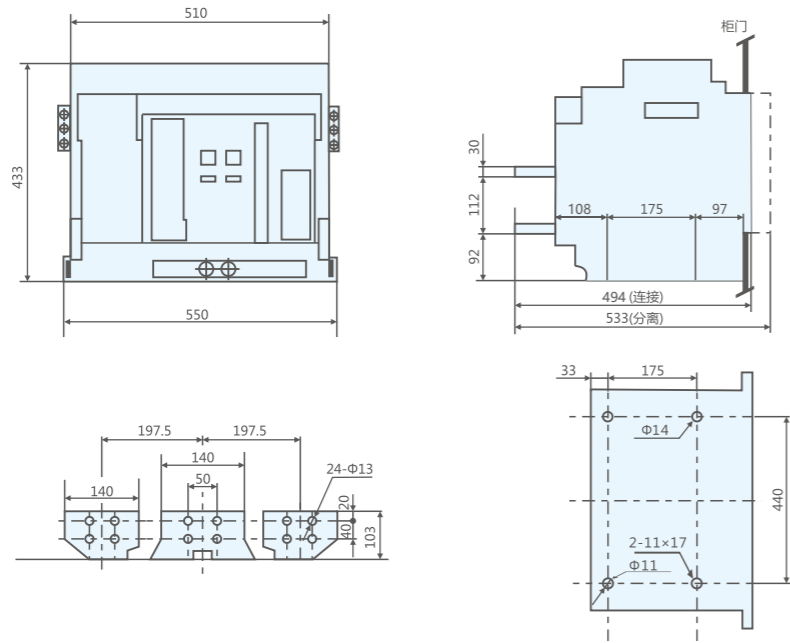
抽屉式断路器安装尺寸及外形尺寸 (FTW3-4000/3, In=3600A、4000A)
